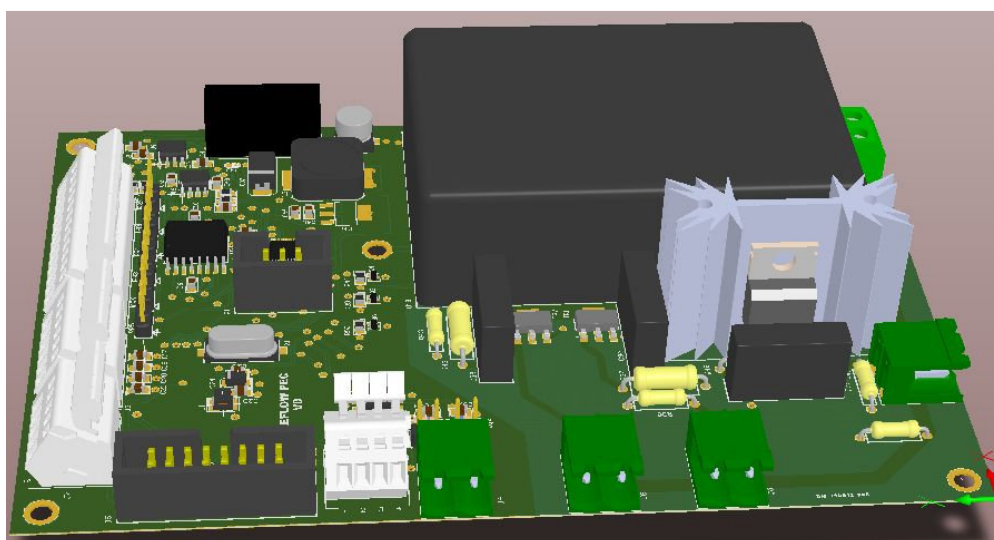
Ukážka návrhu – TOP a BOTTOM vrstva
